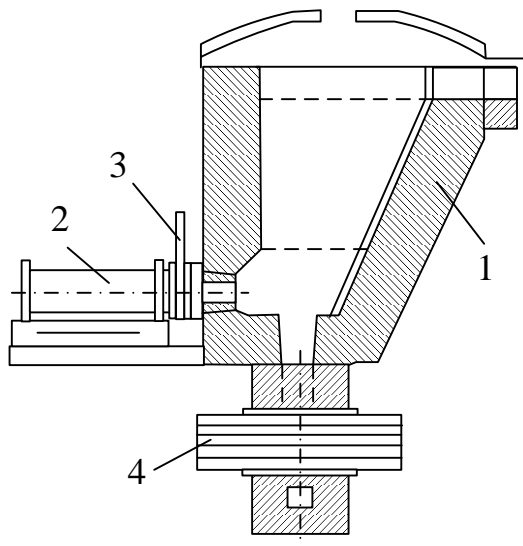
Металлоприемник горизонтальной МНЛЗ конструкции фирмы «ФЕСТ-Альпине: 1 – корпус; 2 – кристаллизатор; 3 – шиберный затвор; 4 – индуктор для подогрева металла»
